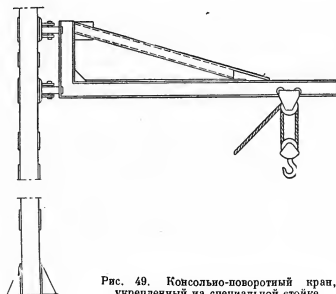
Консольно-поворотный кран, укрепленный на специальной стойке.
